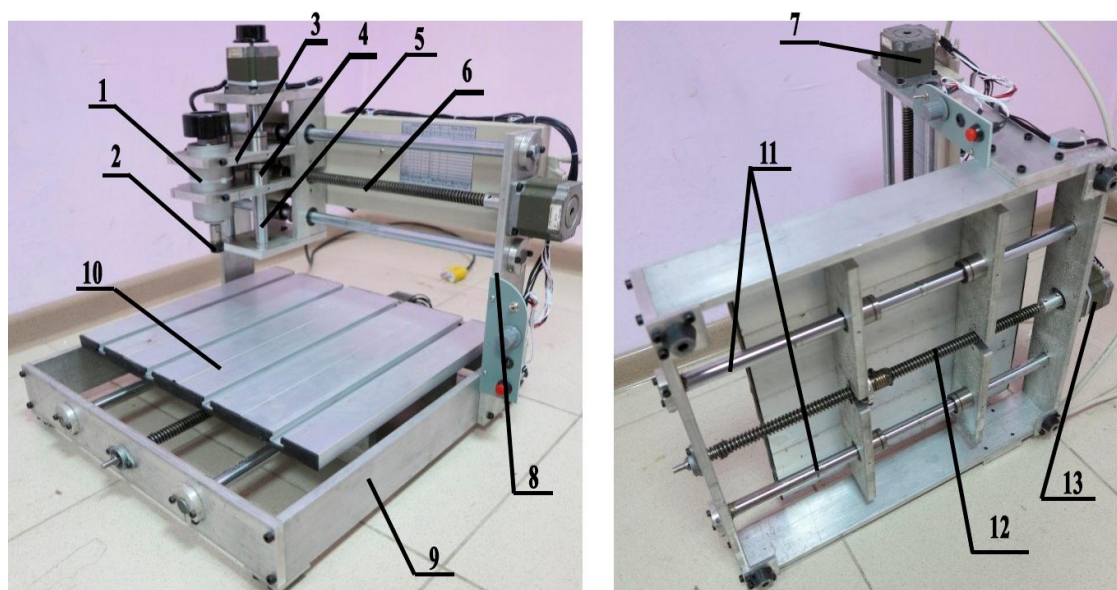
Фрезерний верстат CNC-2535AL2
